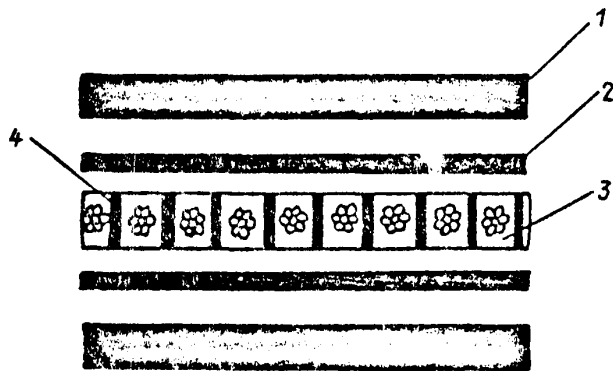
Схема сборки стыка резинокросовой ленты:
